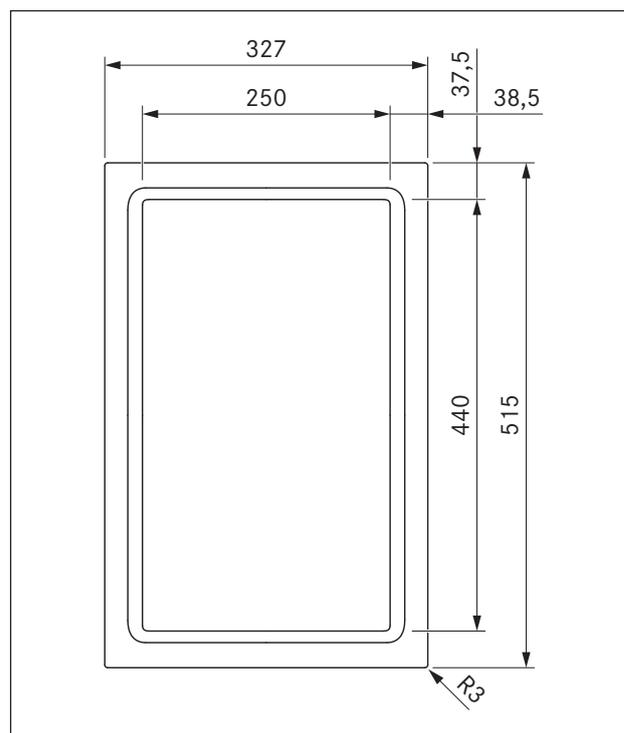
Dimensões do aparelho CKT, vista de cima
